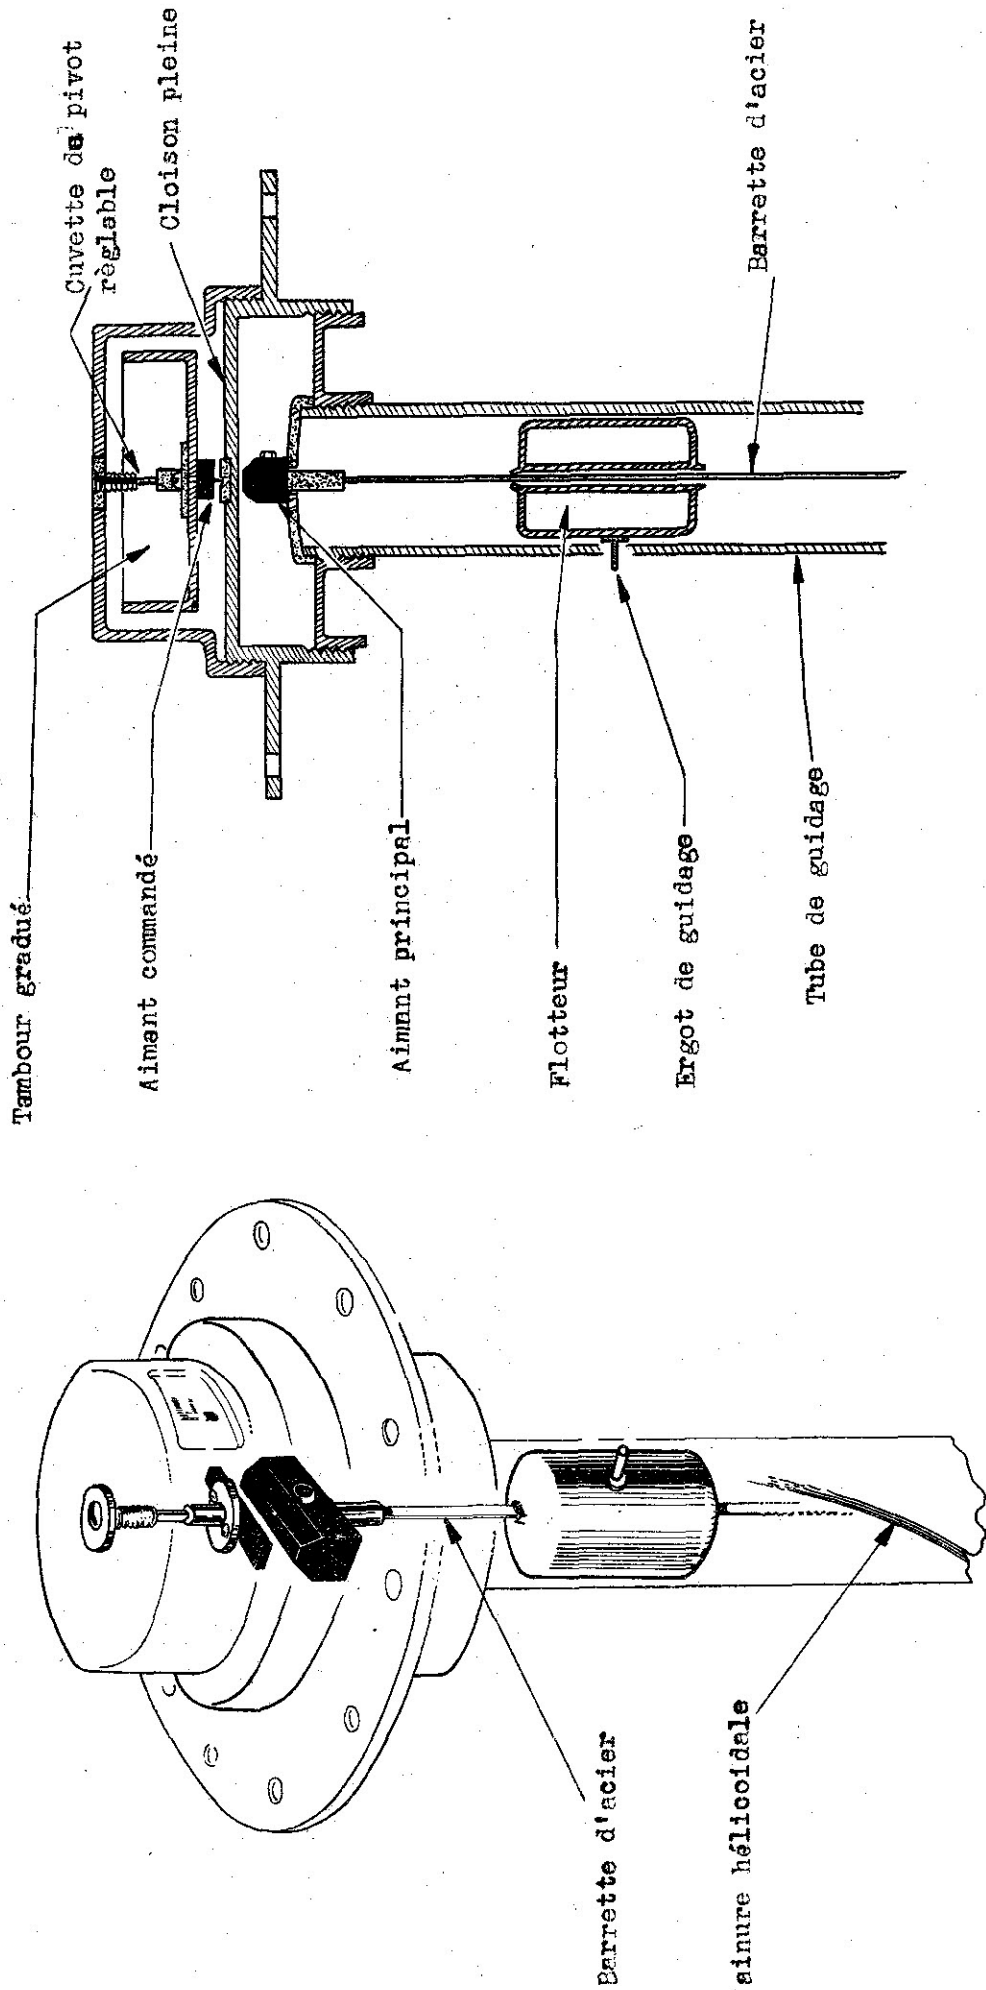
Jauge de contenance de carburant à flotteur rotatif. Vue en coupe
